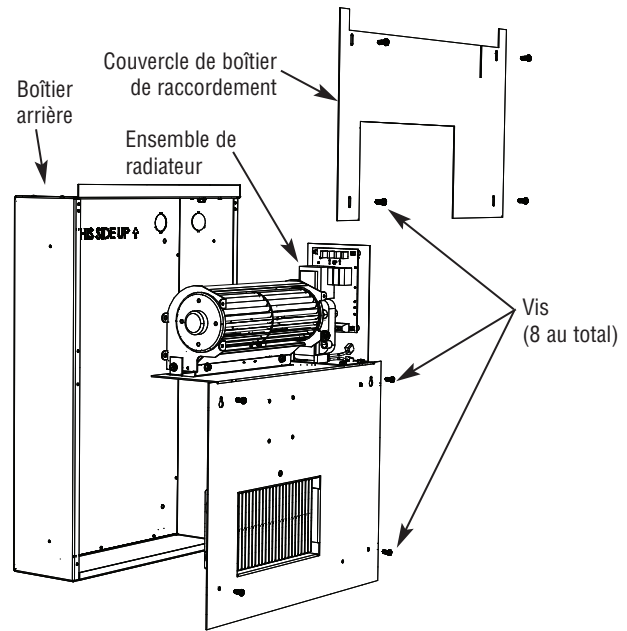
Démontage de l'ensemble de radiateur du boîtier arrière
